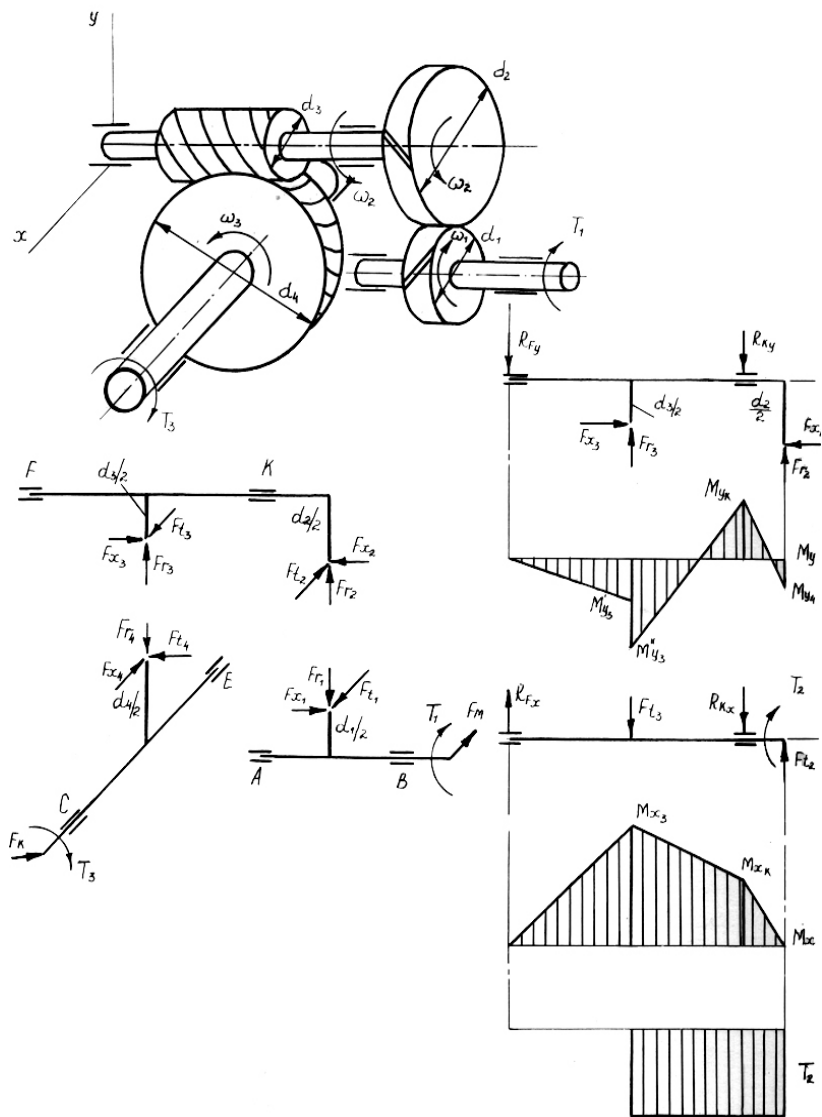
Зубчато-червячная передача с первой цилиндрической косозубой ступенью
